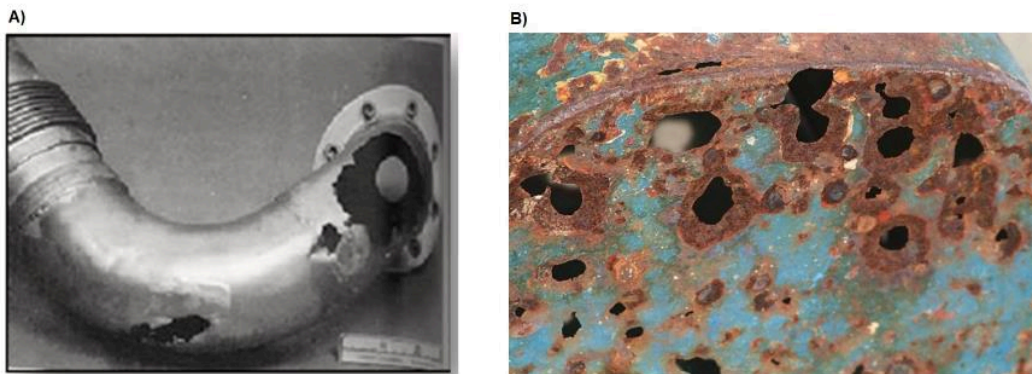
Exemples de corrosió per erosió. A) Canonada en forma de colze. B) Equip industrial. [34]
